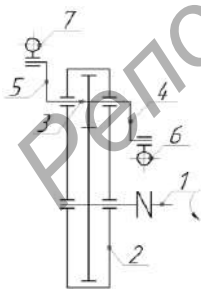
Схема механизма для двухтросового привода рабочего оборудования
